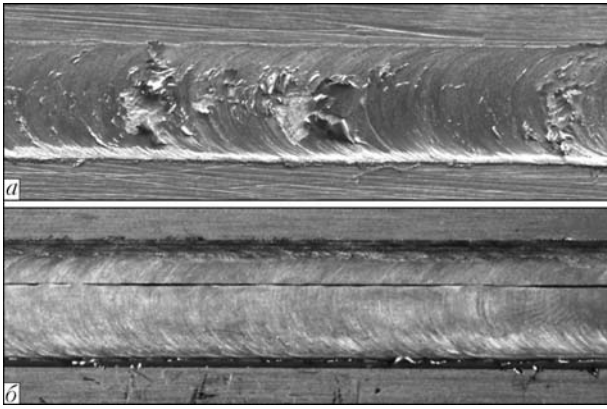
Внешний вид ($\times 2$) лицевой поверхности швов, полученных СТП алюминиевого сплава 1420 толщиной 2 мм при чрезмерном (а) и недостаточном (б) погружении бурта в свариваемый металл
